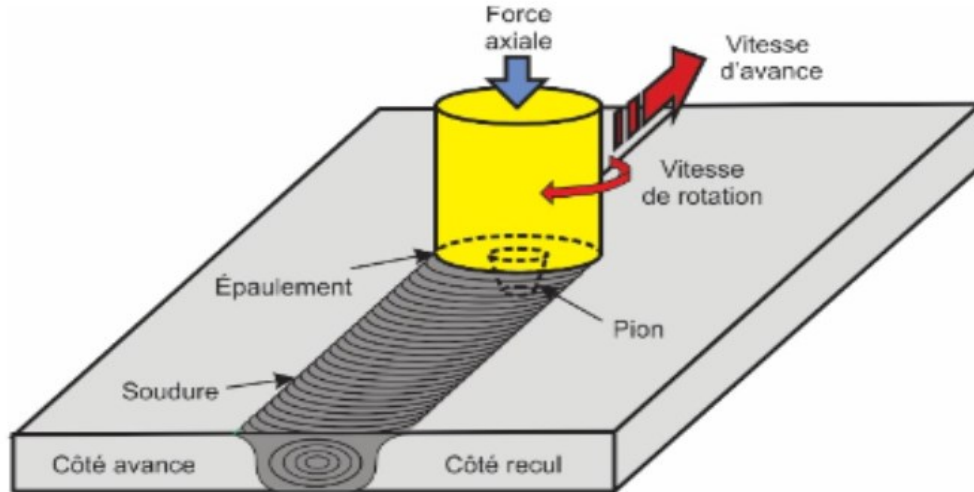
Définitions des termes lors du soudage par friction malaxage (FSW) [9].
